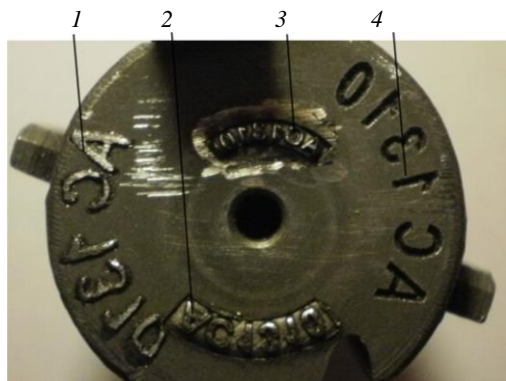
Чашка затвора гладкоствольного карабина «Вепрь» 12-го калибра с нанесенными баллистическими маркерами: 1 – наплавка металла с использованием импульсной лазерной сварки; 2 – литерный способ с высоким шрифтом; 3 – литерный способ микротекста в прикапсюльной зоне; 4 – выборка металла гравером
